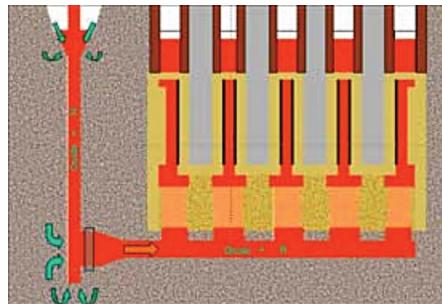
Заливка «сырой» формы 4-цилиндрового блока двигателя, верхний метод
